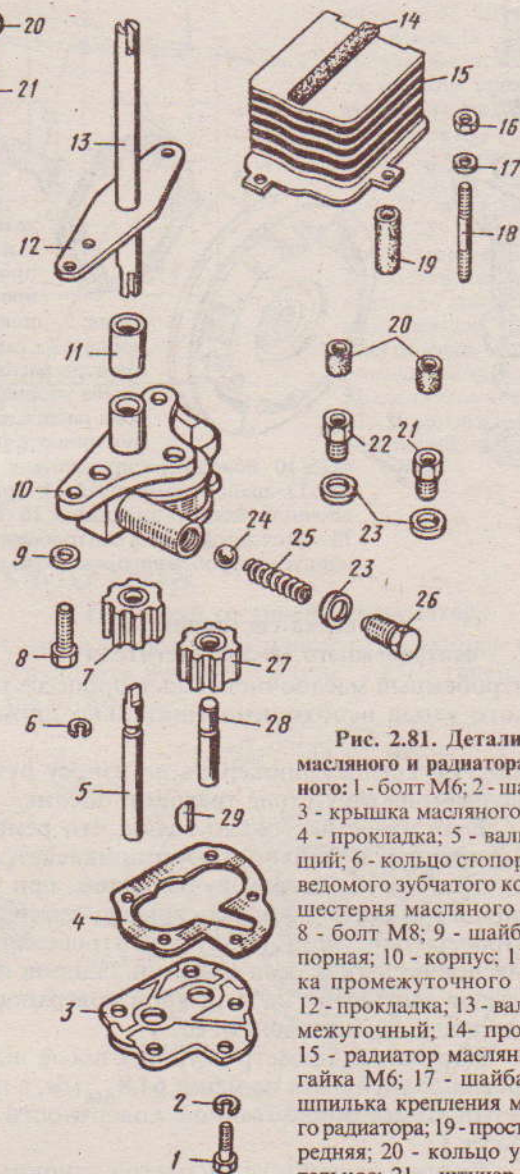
Детали насоса масляного и радиатора масляного: 1 - болт М6; 2 - шайба 6Т; 3 - крышка масляного насоса; 4 - прокладка; 5 - валик ведущий; 6 - кольцо стопорное оси ведомого зубчатого колеса; 7 - шестерня масляного насоса; 8 - болт М8; 9 - шайба 8 стопорная; 10 - корпус; 11 - втулка промежуточного валика; 12 - прокладка; 13 - валик промежуточный; 14 - прокладка; 15 - радиатор масляный; 16 - гайка М6; 17 - шайба 6; 18 - шпилька крепления масляного радиатора; 19 - прокладка передняя; 20 - кольцо уплотнительное; 21 - штуцер отводящий; 22 - штуцер подводящий; 23 - прокладка; 24 - шарик Б 11,509-200; 25 - пружина редукционного клапана; 26 - пробка редукционного клапана; 27 - зубчатое колесо ведомое масляного насоса; 28 - ось ведомого зубчатого колеса; 29 - шпонка 3х5
